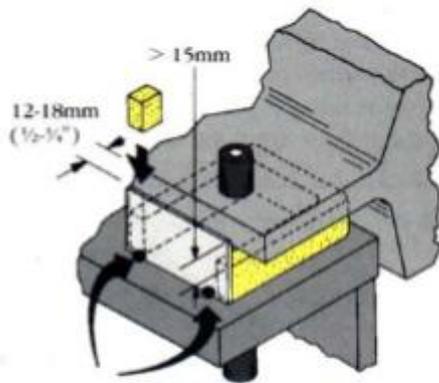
Soldar provisionalmente la chapa del encofrado. Insertar los componentes del bebedero.
